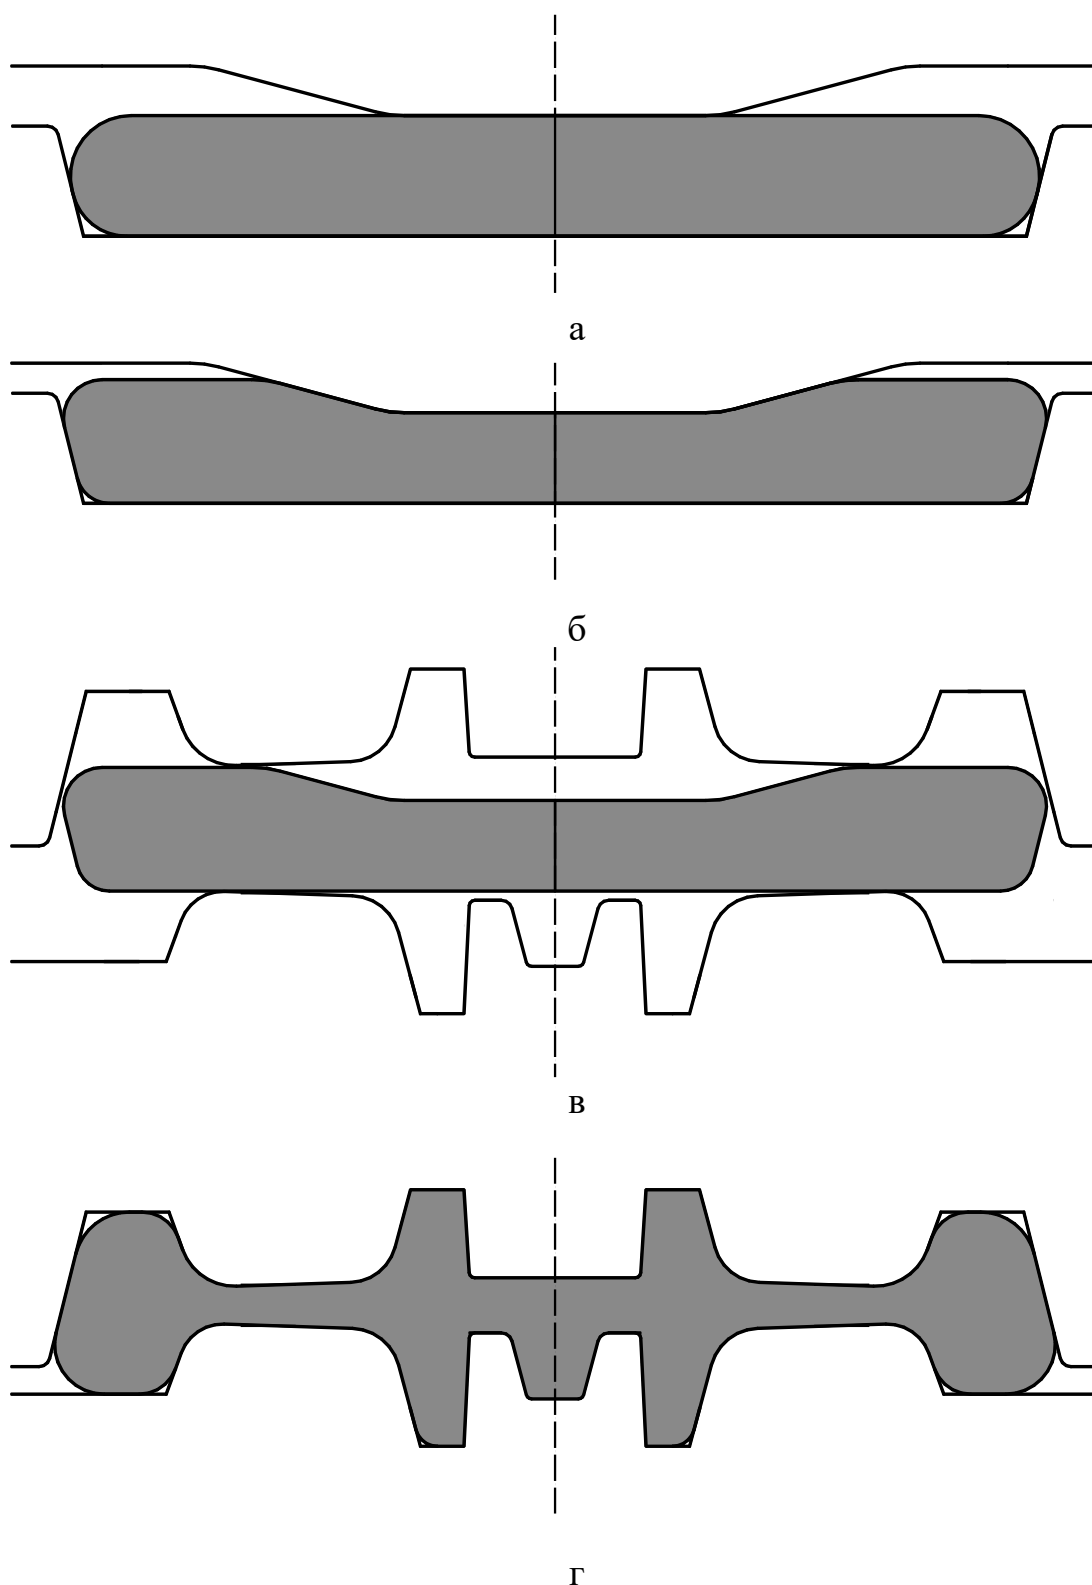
Технологическая схема разгонки заготовок конусной плитой на прессе силой 50 МН и штамповки колесных заготовок на прессе силой 100 МН
